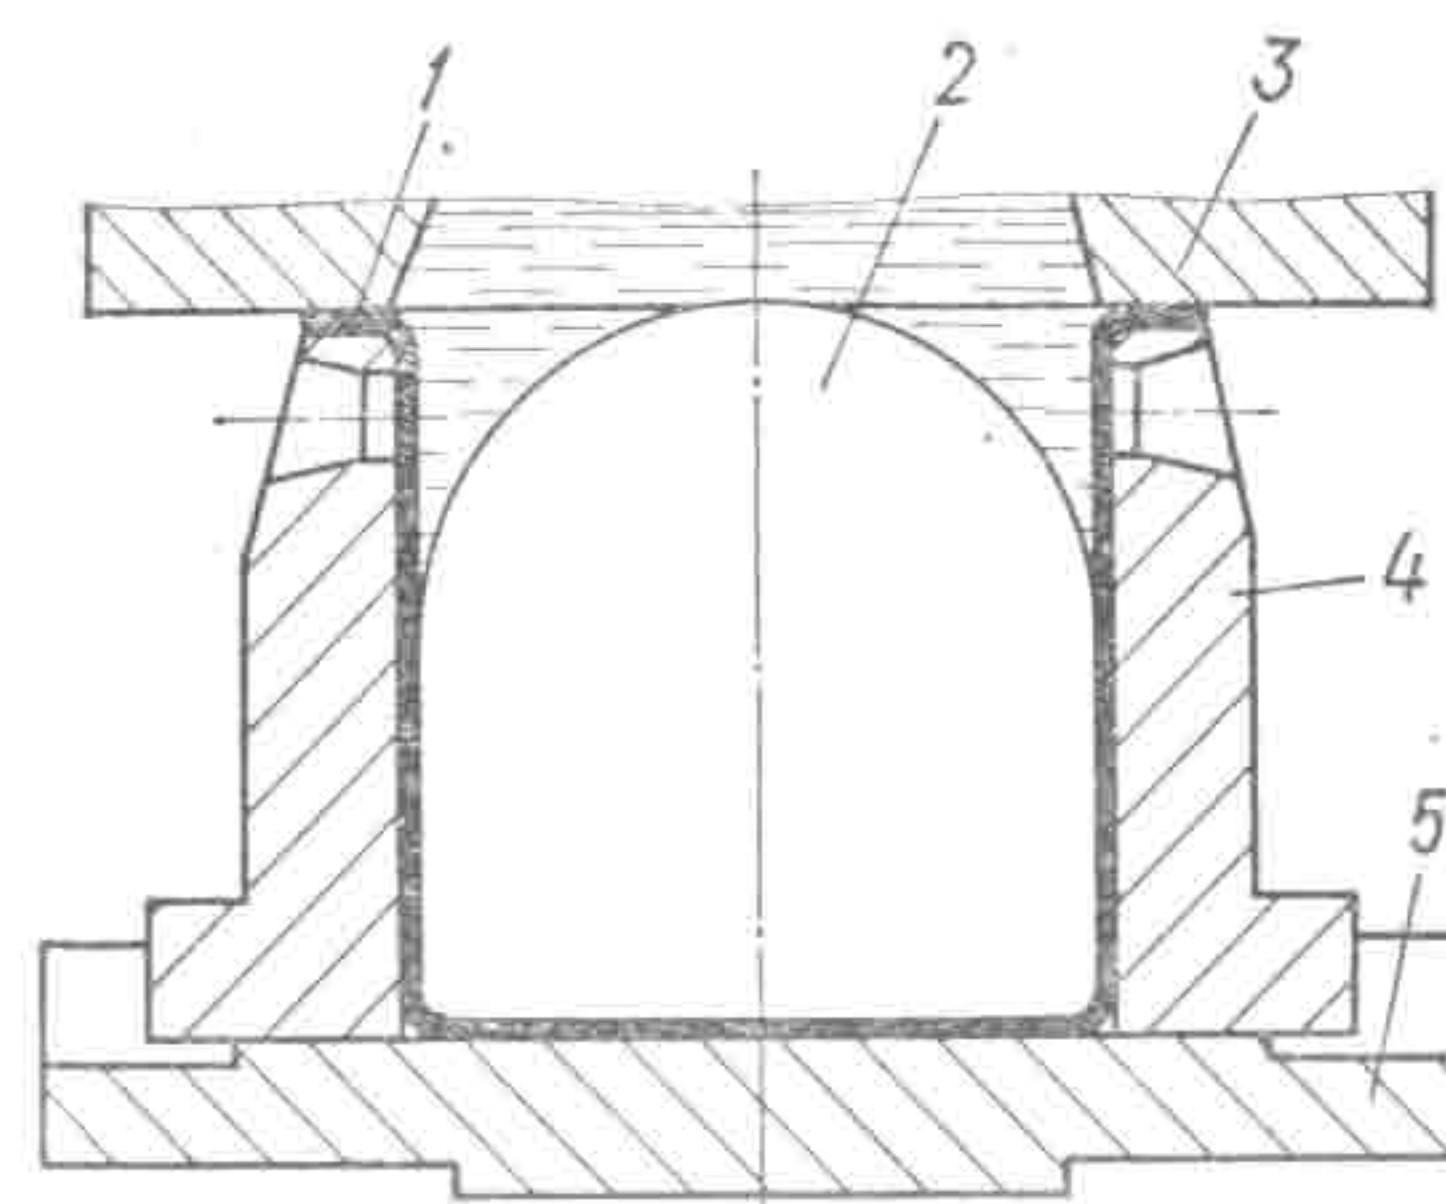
Схема оснастки для пробивки отверстий в цилиндрических заготовках.
